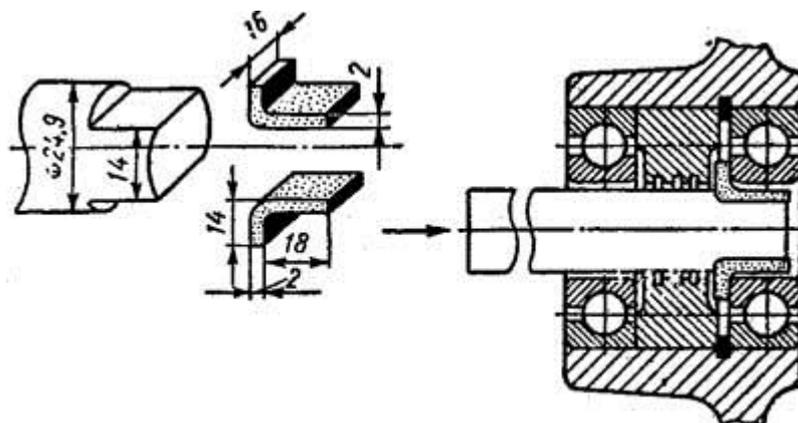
Приспособление для выпрессовки коренных подшипников из картера двигателя, применяемое вместе с универсальным съемником
